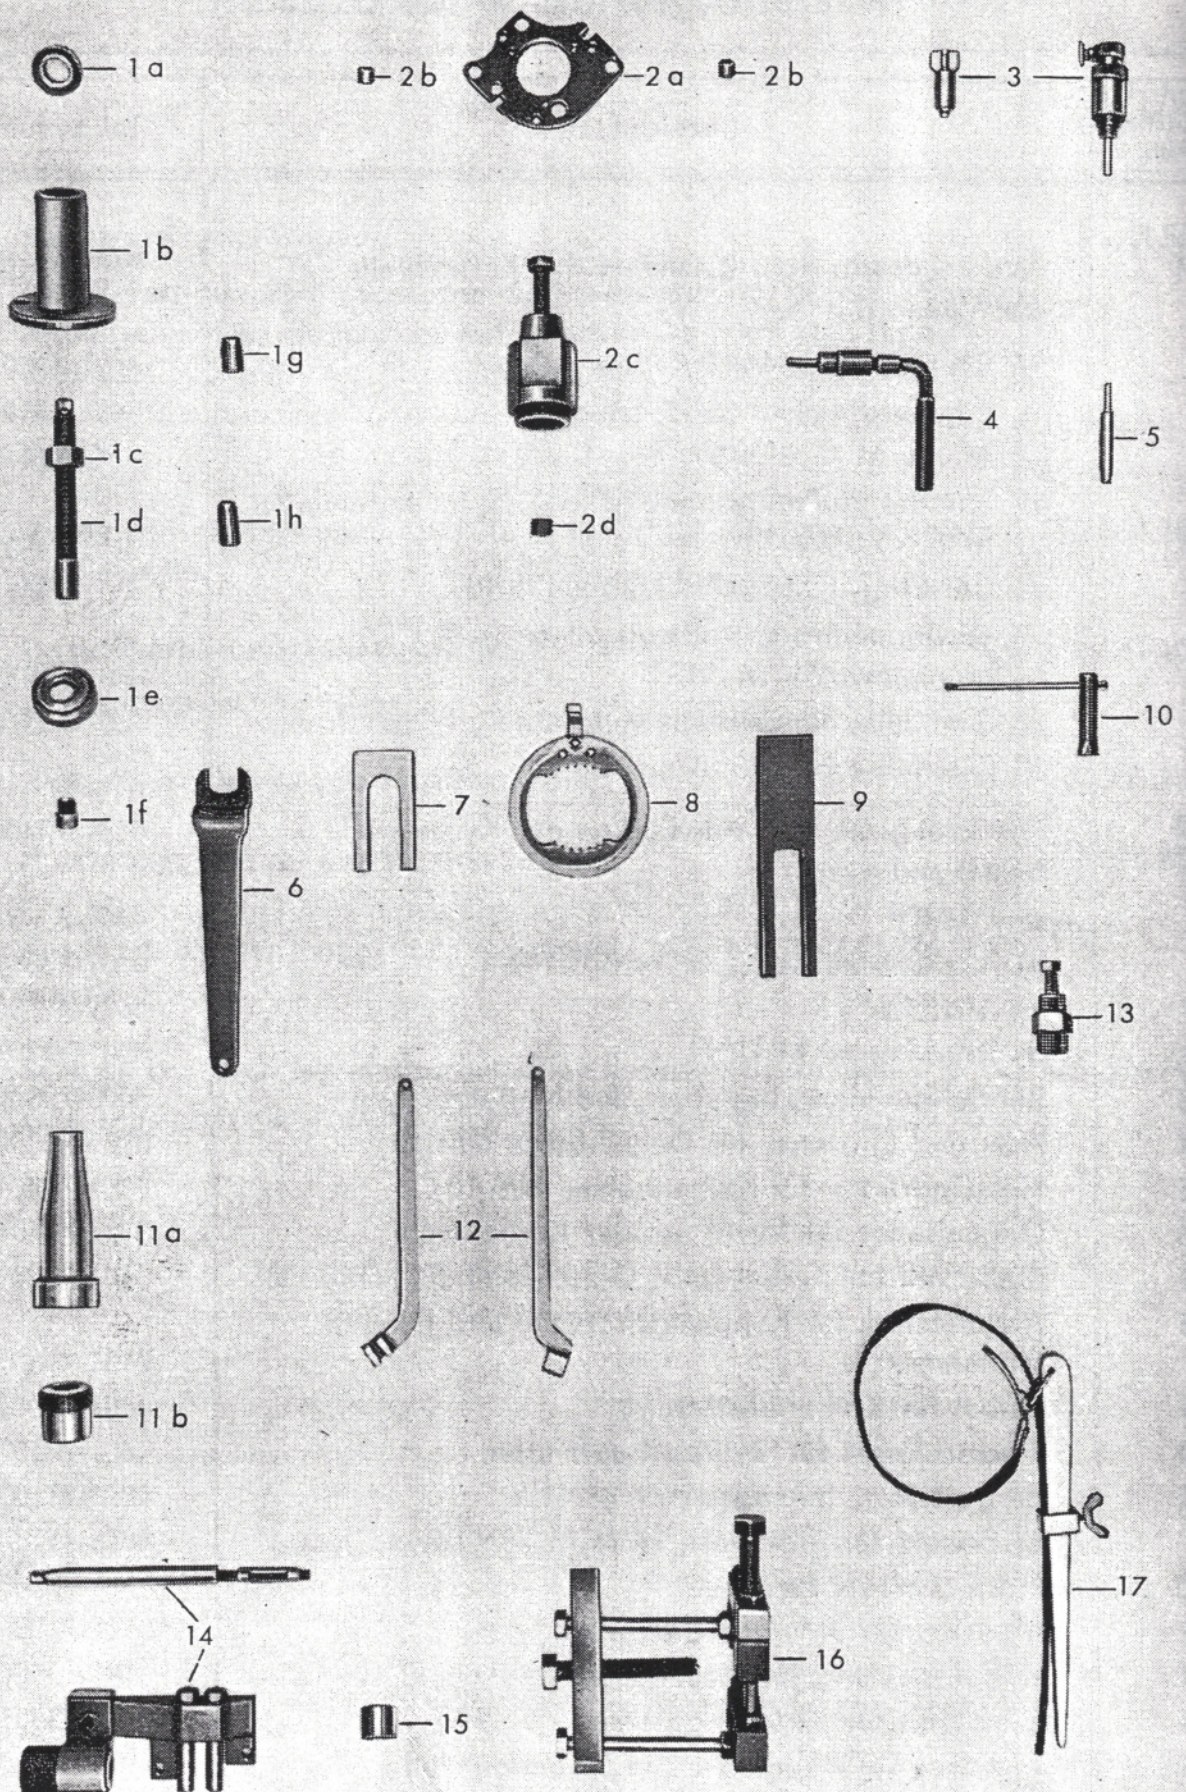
DKW-Spezialwerkzeuge für die DKW Hummel
